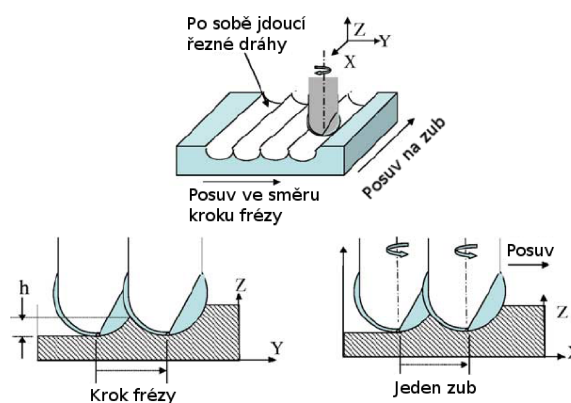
Geometrie a souřadnicový systém frézy s kulovou hlavou [2]
